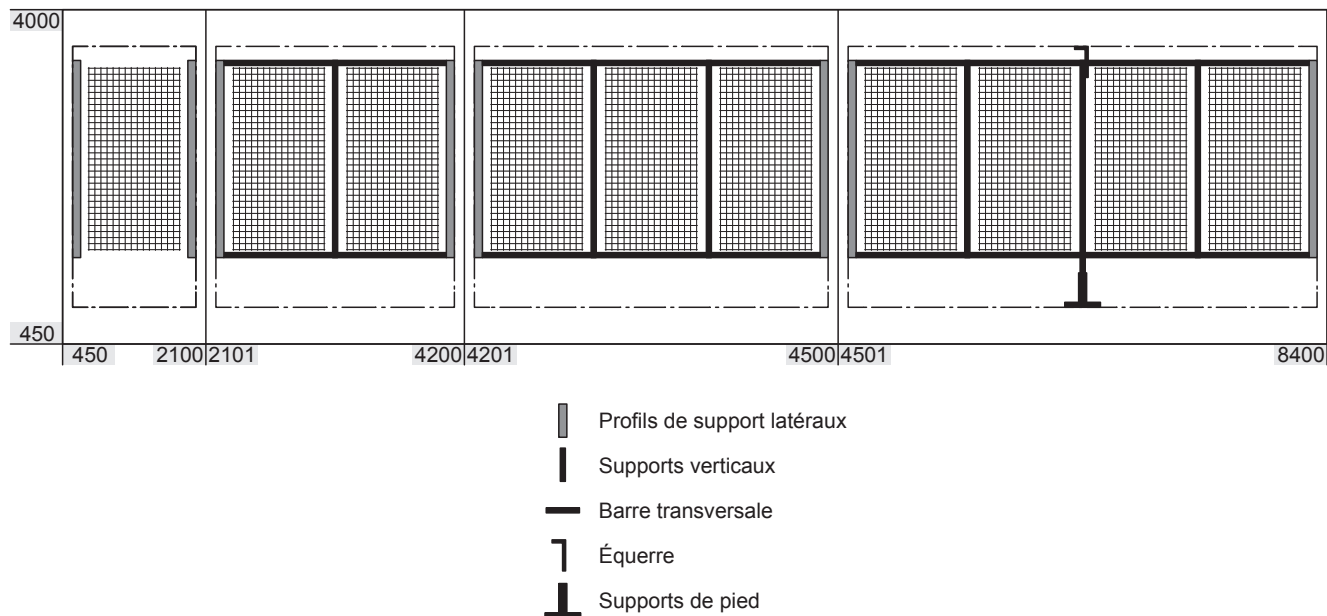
Aperçu des constructions-cadre du système de buses (dimensions de l'intérieur du conduit en mm)
